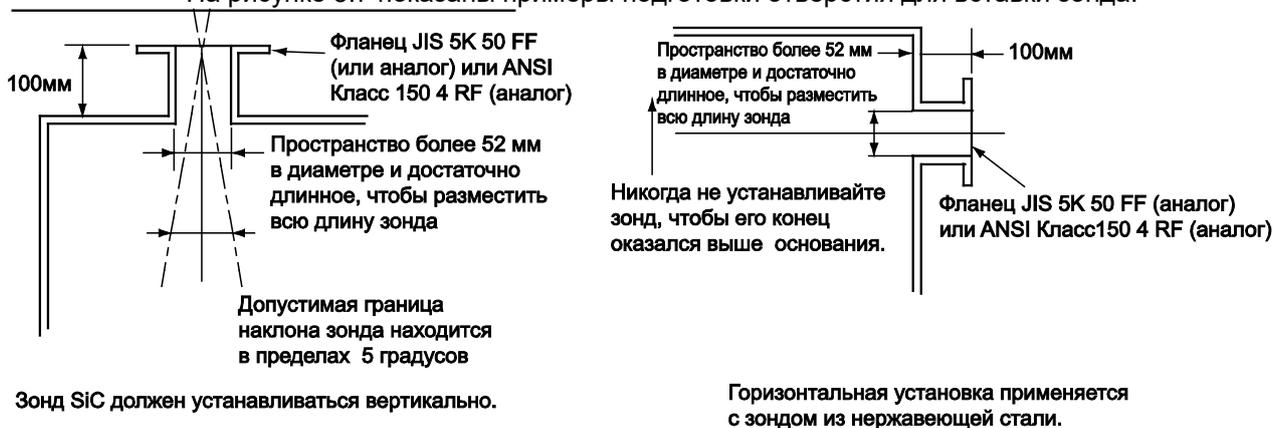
Примеры подготовки отверстия для вставки зонда
